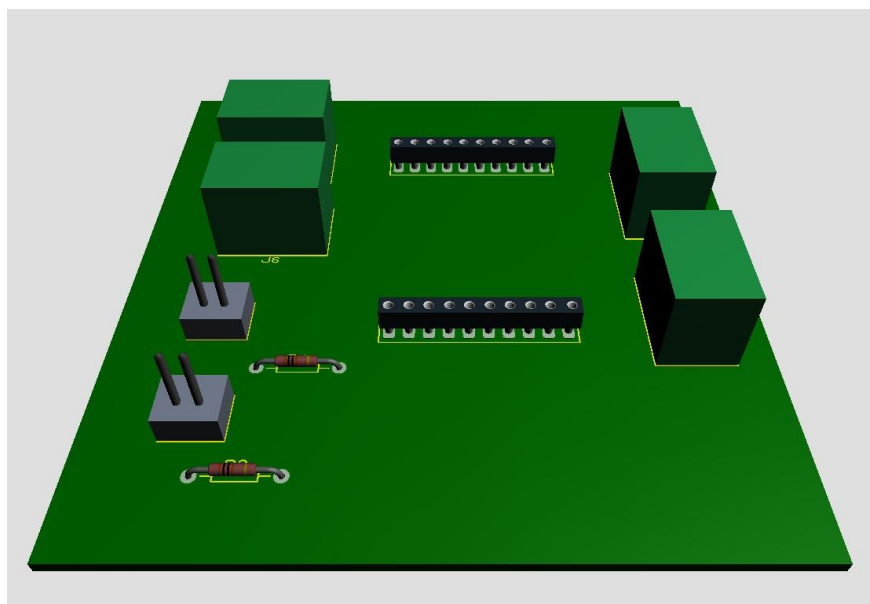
Diseño de la PCB, con el socket para el microcontrolador
